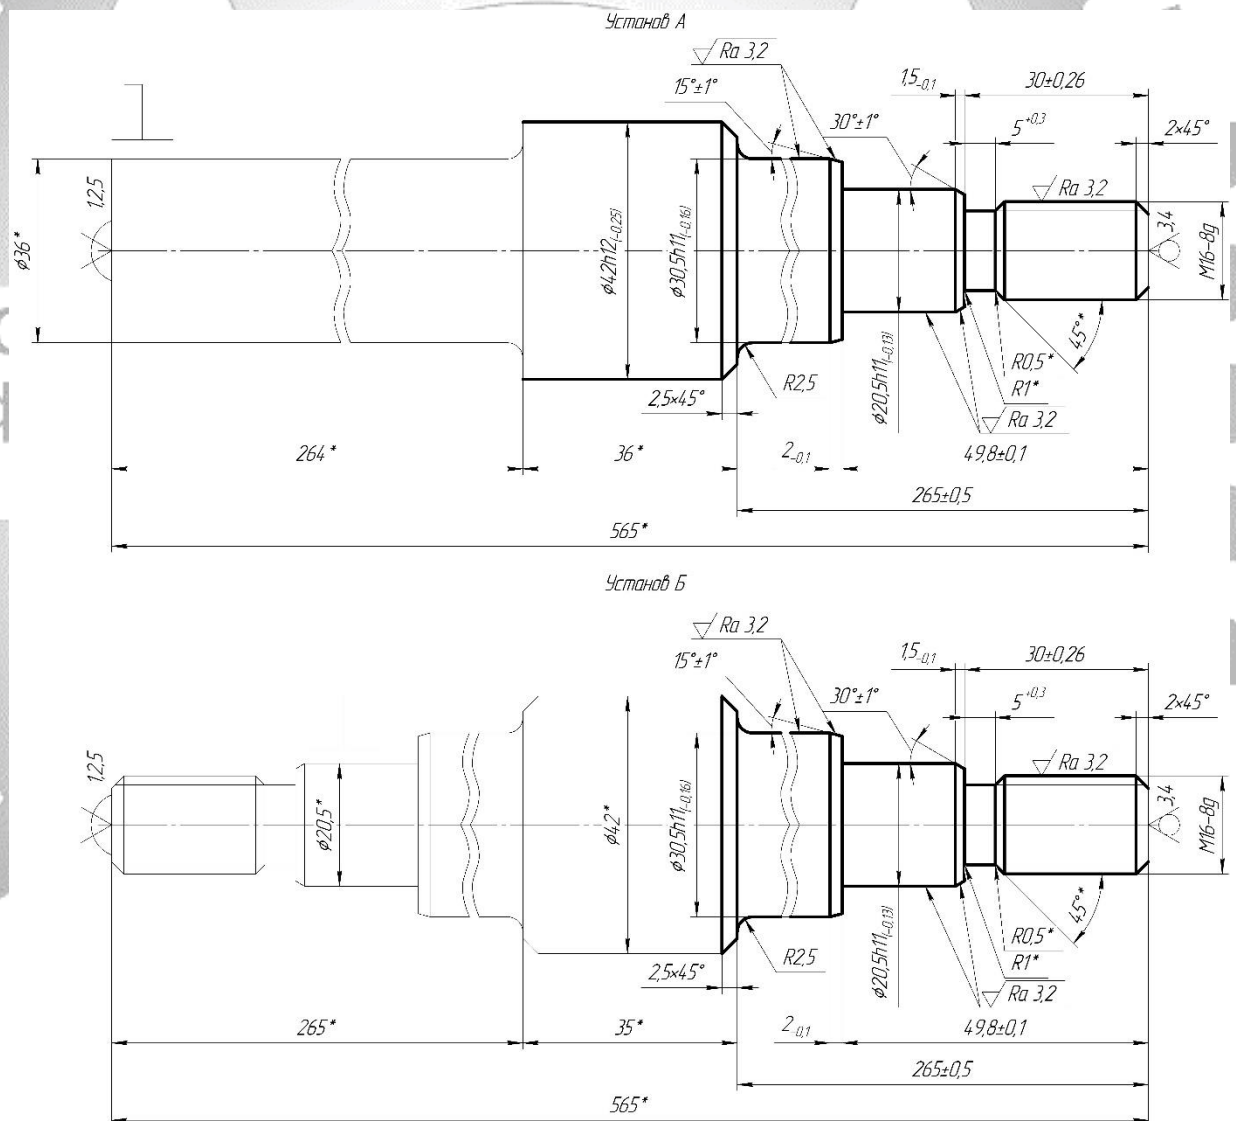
Схема базування заготовки на токарній з ЧПК операції (перший варіант)
